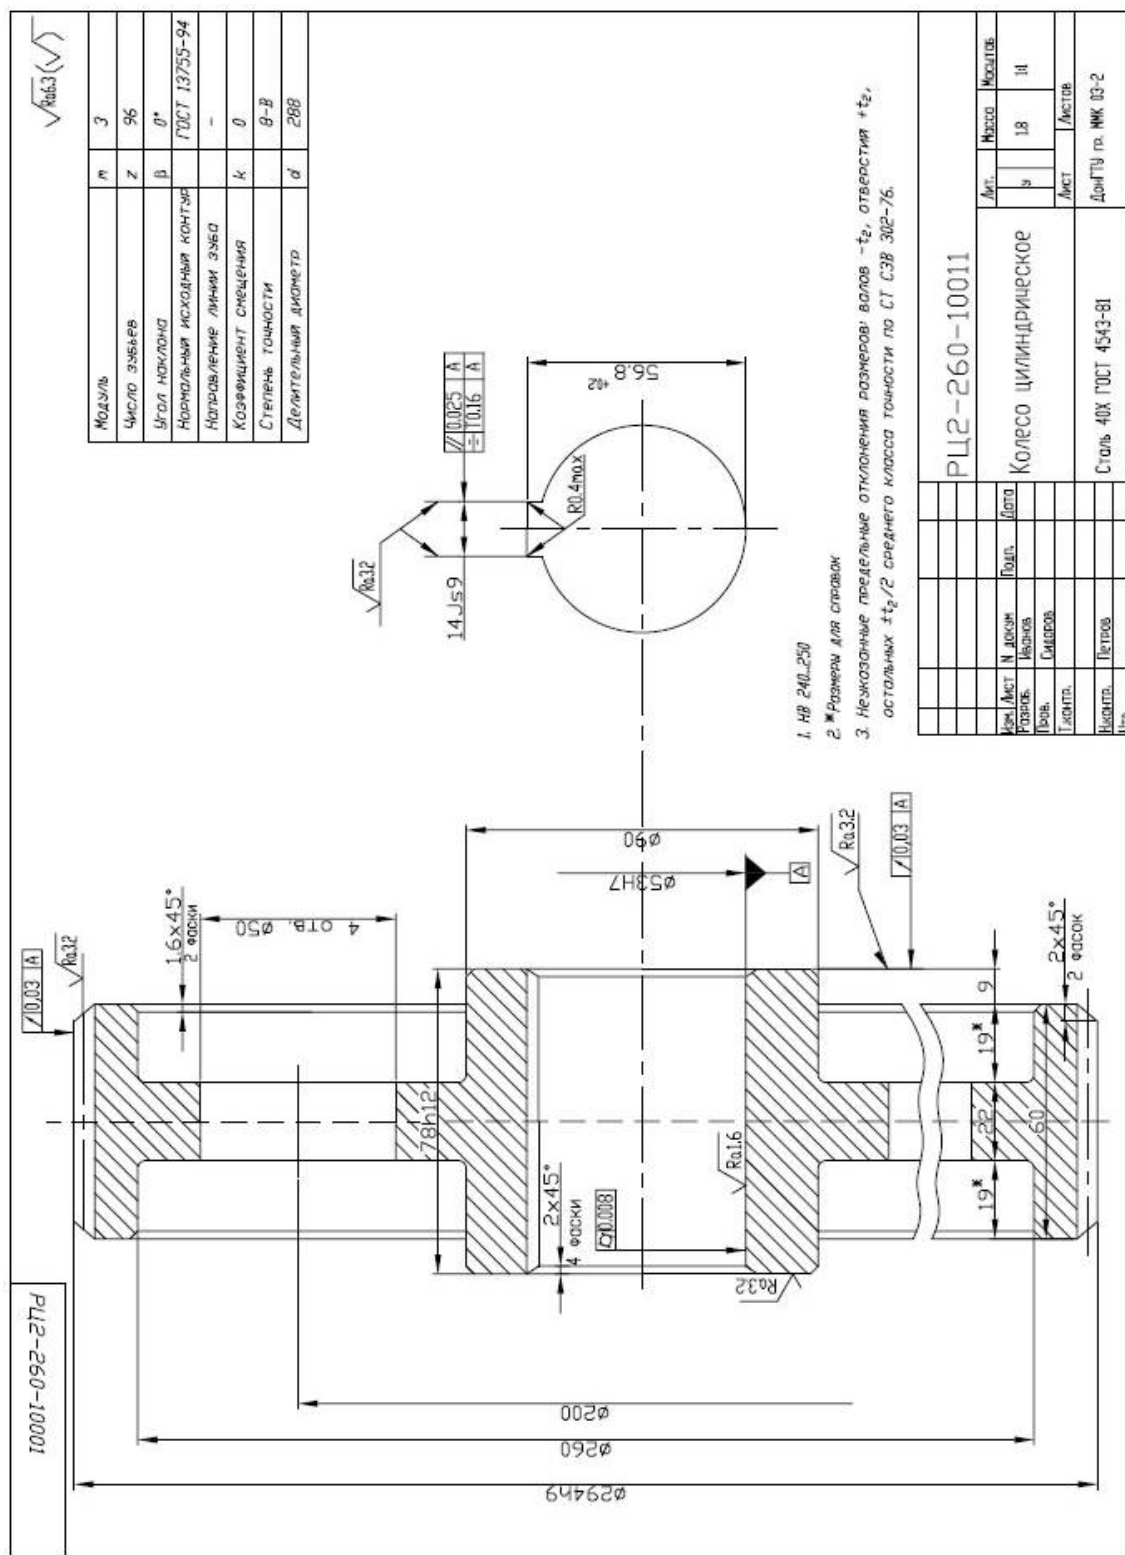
Укрупненный вид деталировки зубчатого редуктора на рисунке К.6
